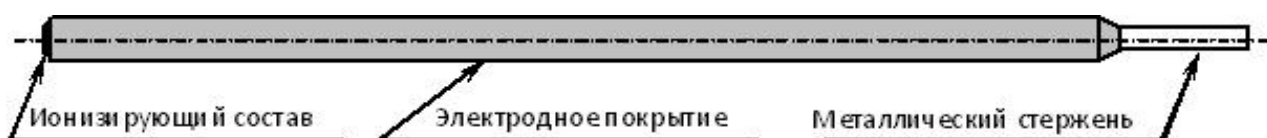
Внешний вид покрытого электрода для ручной дуговой сварки
